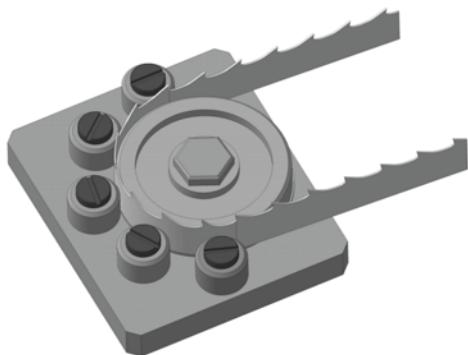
Приспособление для проведения упругопластического деформирования ленточной пилы на одном шкиве с прижимными роликами
